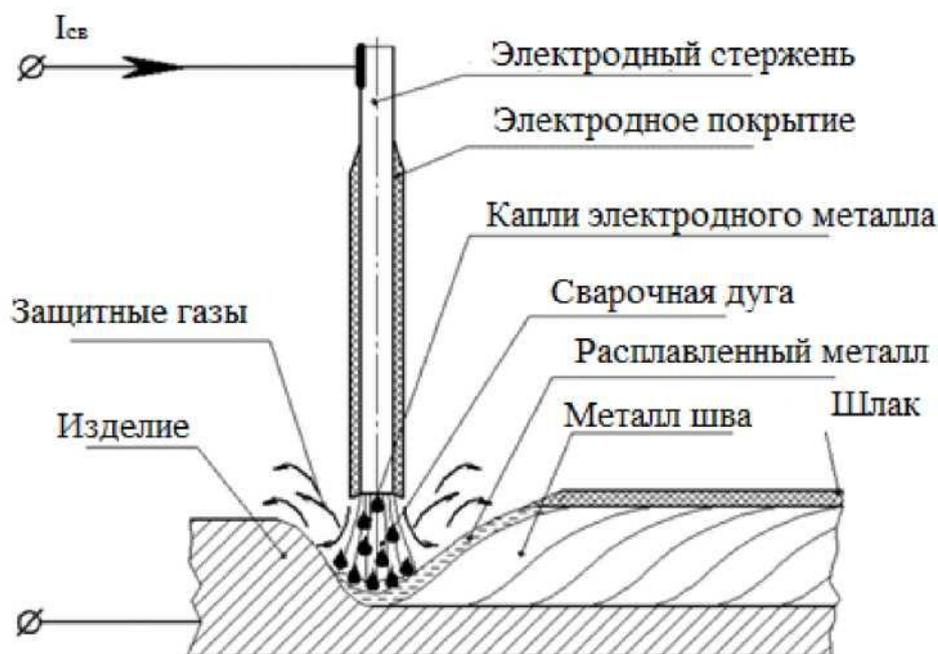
Схема ручной дуговой сварки покрытым электродом
